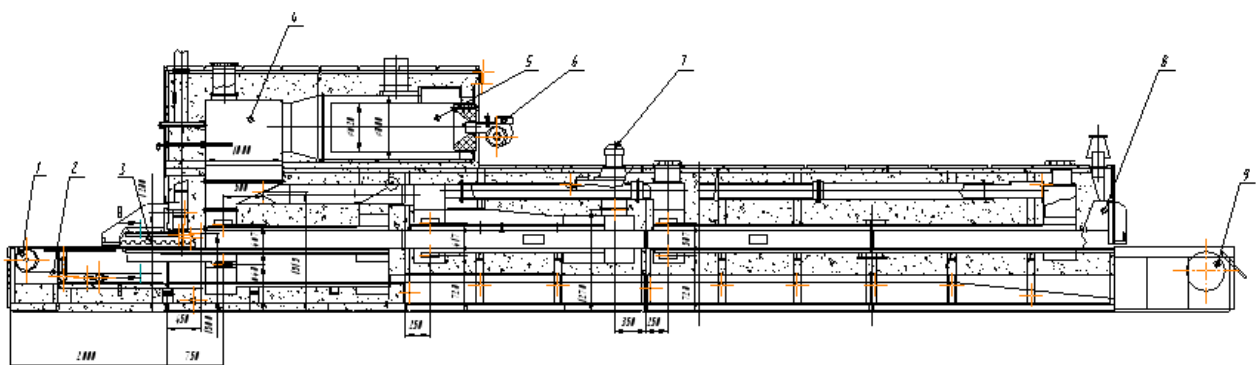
Розріз печі А2-ХПН-25: 1 – натяжний барабан, 2 – сітчастий под, 3 – зволожувач, 4 – камера змішування, 5 – газовий пальник, 6 – вентилятори рециркуляційні, 7 – конвективний вентилятор, 8 – витяжка, 9 – привідний барабан.
